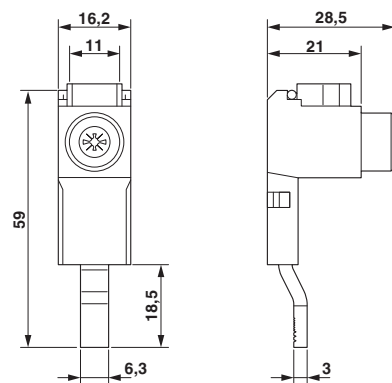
Dimensions de TMC 7 B2/3 TERM PIN
